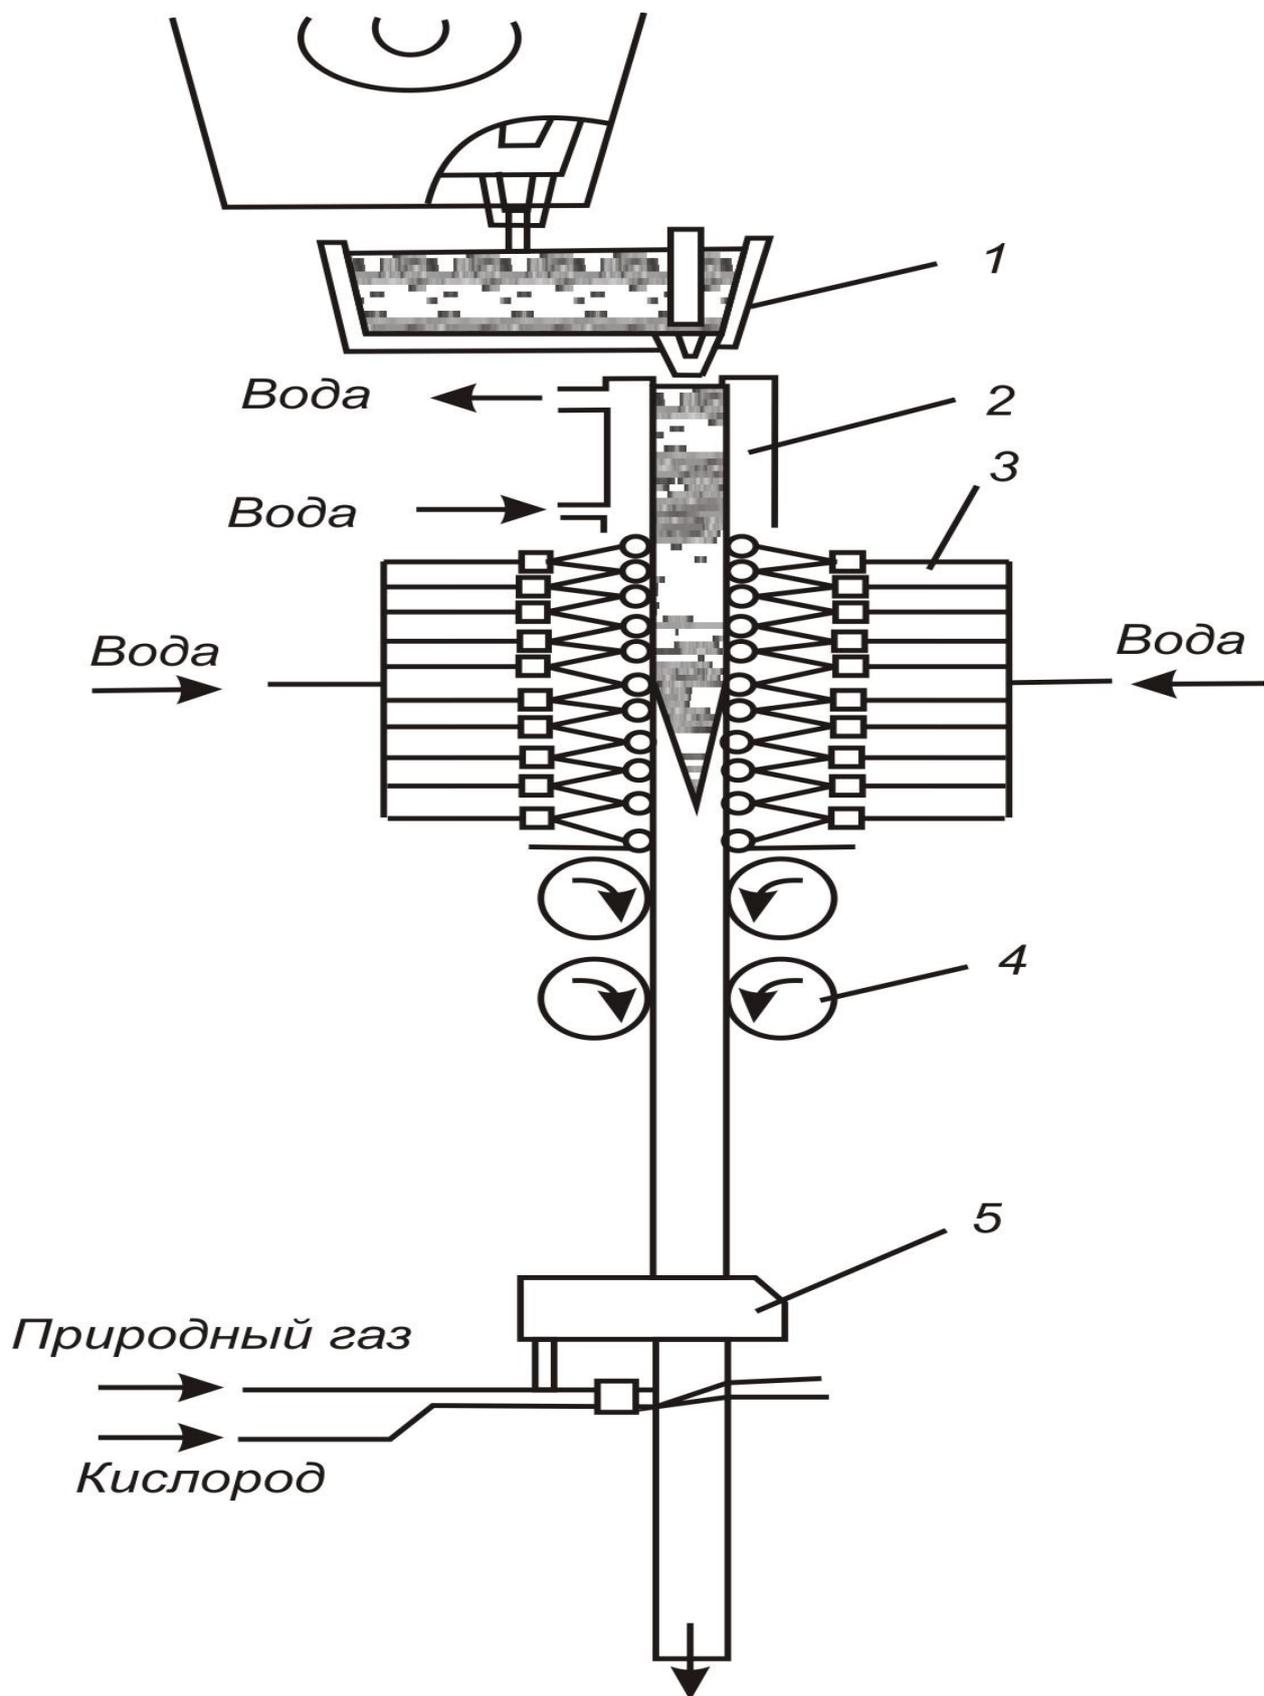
Схема УНРС вертикального типа: 1- промежуточный ковш; 2-кристаллизатор; 3- вторичное охлаждение; 4 - тянущие валки; 5 - газорезка.
